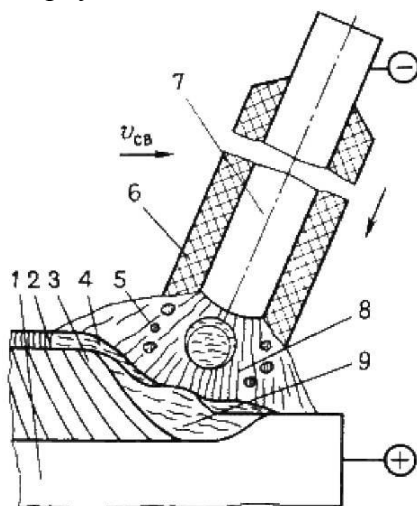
Схема процесса сварки металлическим покрытым электродом
